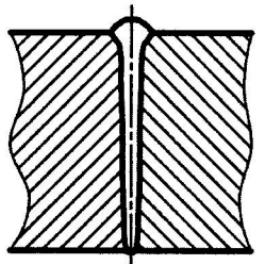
Типова форма зварного шва при ЕПЗ
